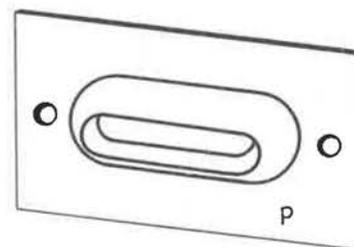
Porte clavetée sur la face trapézoïdale du moule M.
